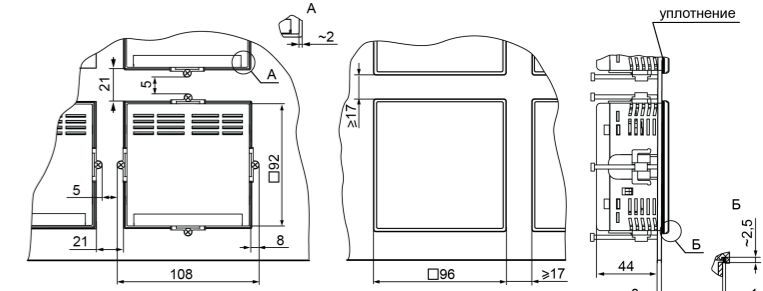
Прибор в корпусе Щ1, установленный в щит толщиной 3 мм
